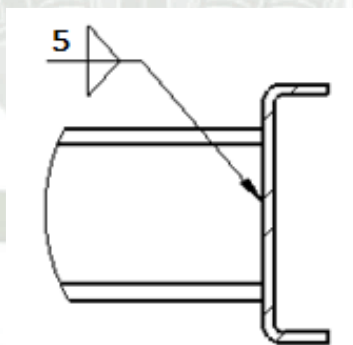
Soldadura Travesaño y Vigas Laterales.
